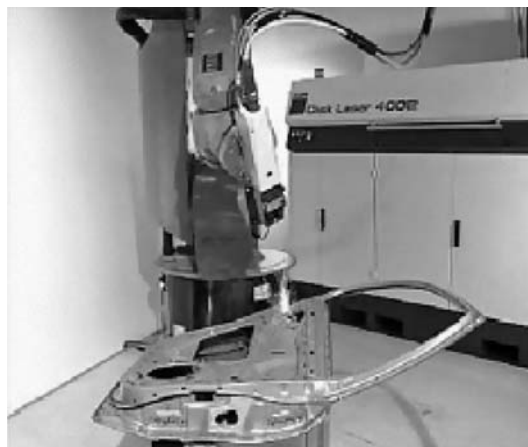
РТК лазерной сварки на базе ПР Kuka KR-125
